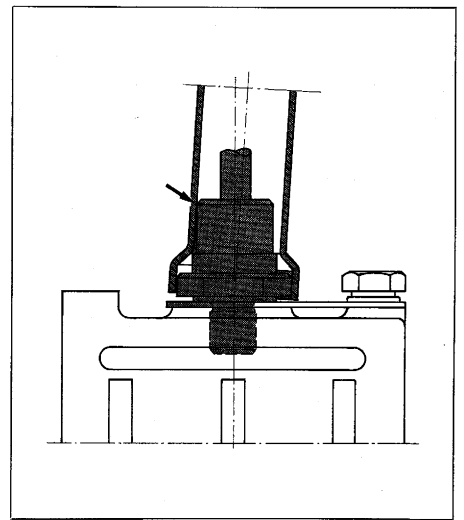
Steckschlüsselverkantung beim Einschrauben von Schraubbauelementen
